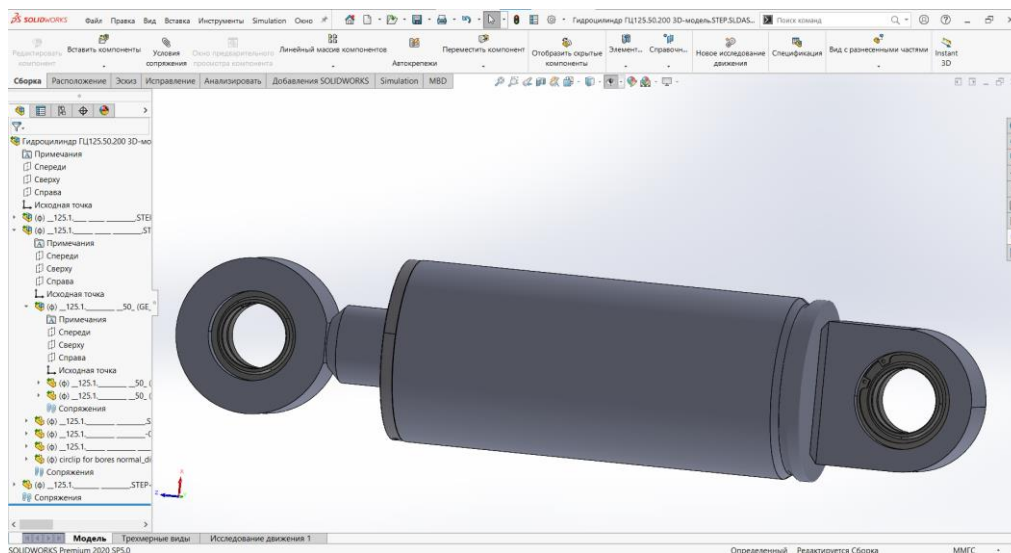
Окно Solidworks Внешний вид 3D-модели гидроцилиндра
